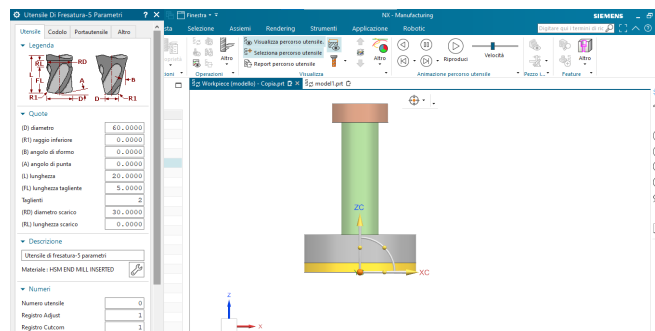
Utensile per Floor Facing, FACE_MILL
